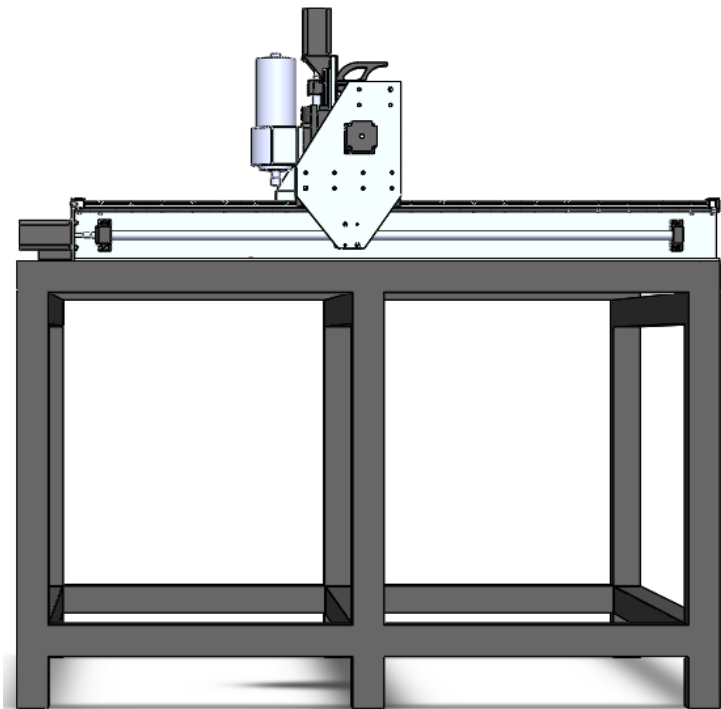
Змодельована збірка фрезерного верстату з ЧПК, вид збоку
